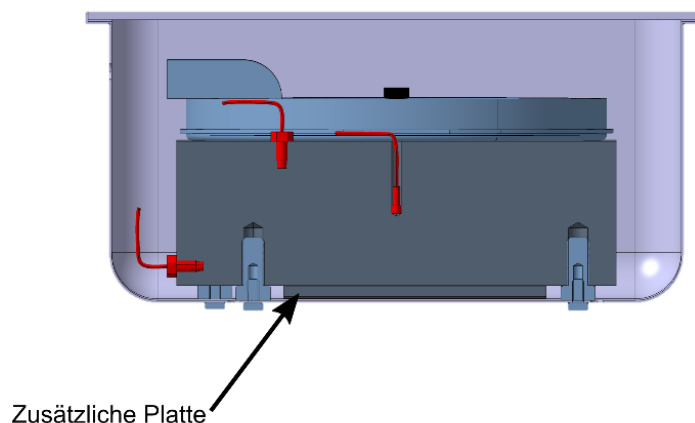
Schnittansicht des Batterie-Dummy mit verbesserter thermischer Anbindung
